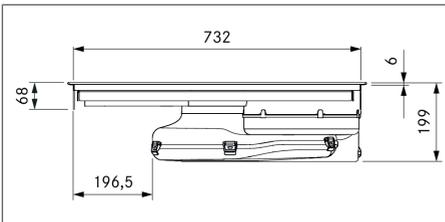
PURU dimensioni apparecchio vista frontale
